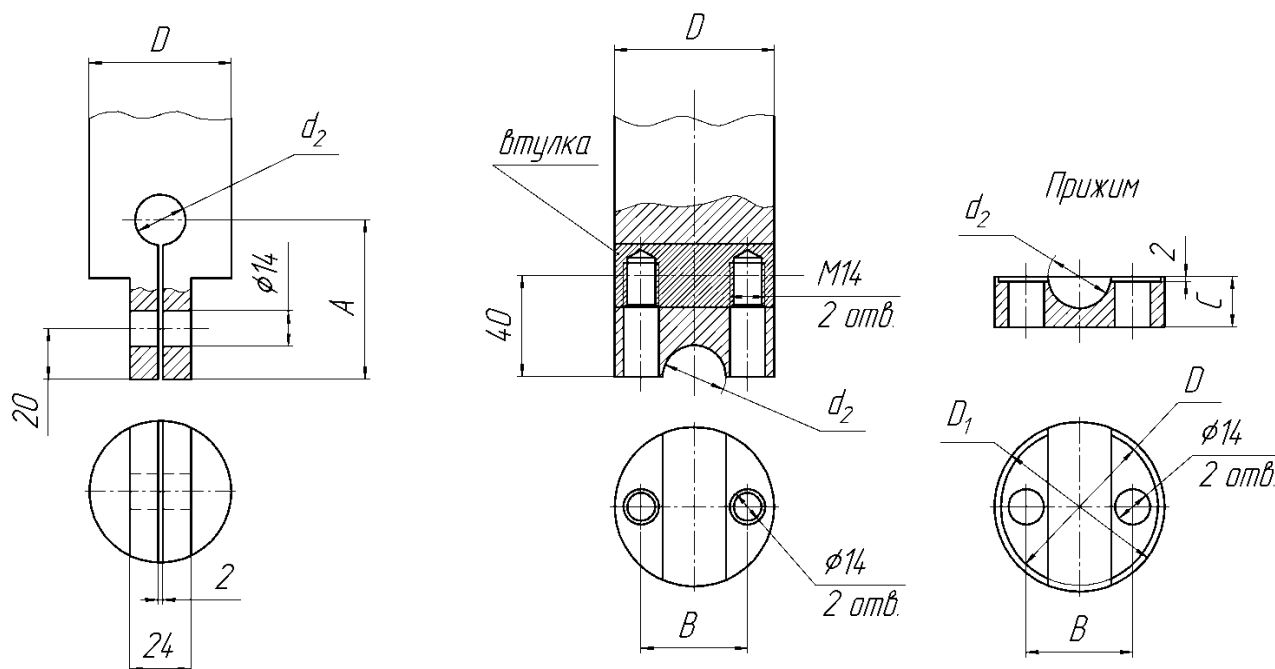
Установочные размеры хоботов контактных сварочных машин
